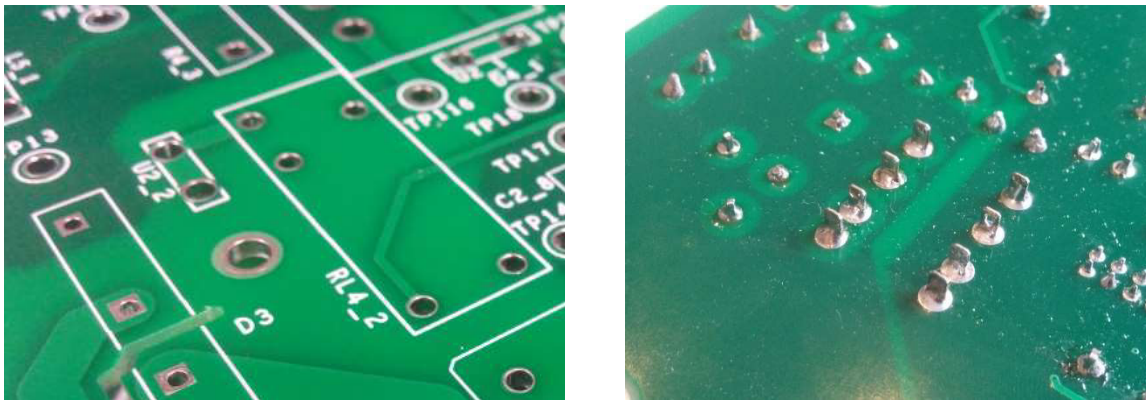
Secuencia de soldadura tipo SMD. Fuente: propio
